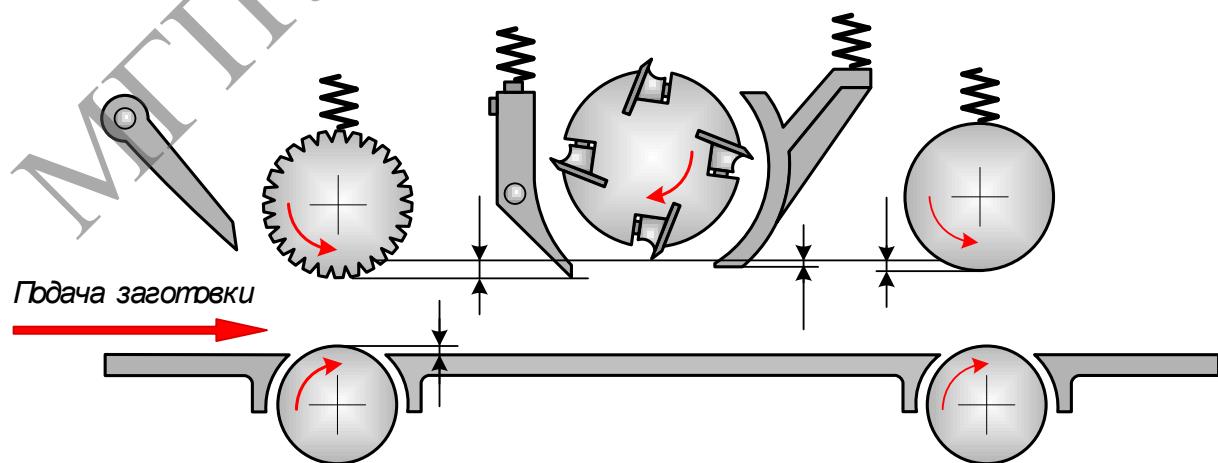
Наладка одностороннего рейсмусового станка
